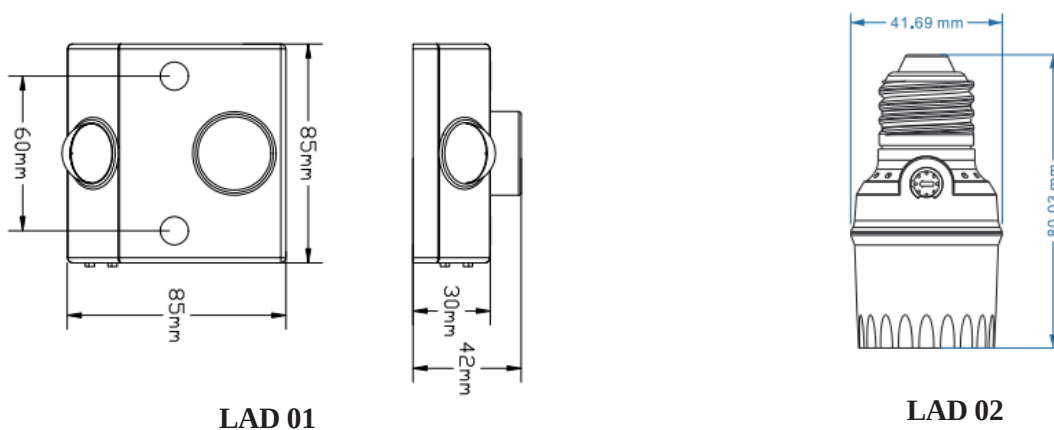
Внешний вид и габаритные размеры датчиков.
